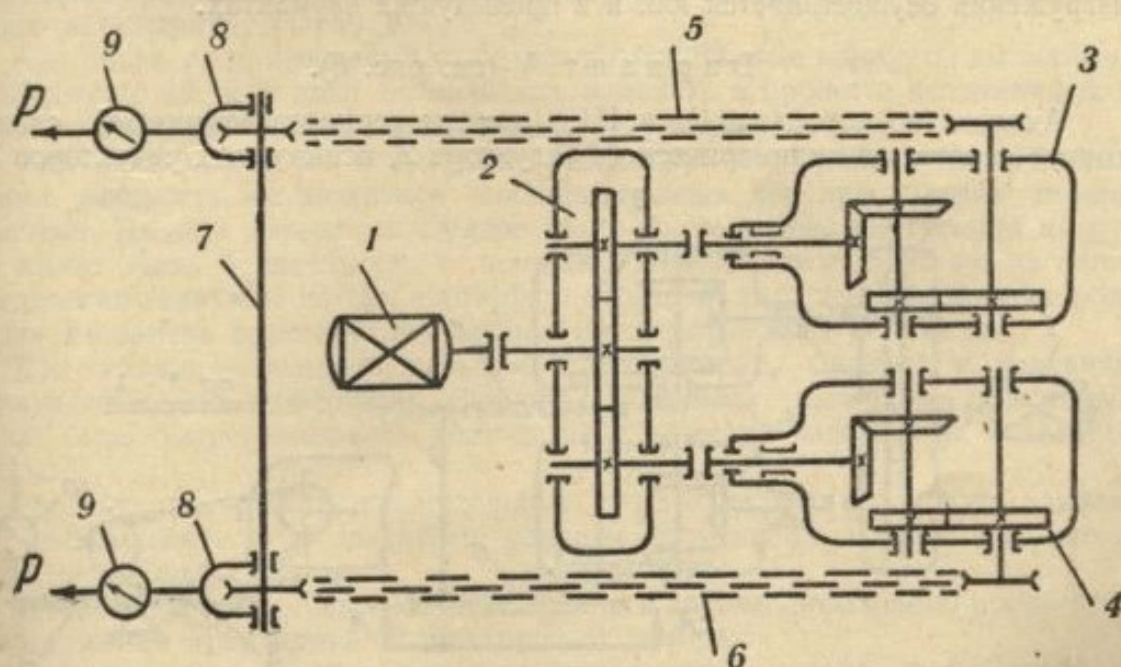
1 — Электродвигатель, 2 — цилиндрический редуктор, 3, 4 — испытуемые редукторы, 5, 6 — втулочно-роликовая цепь, 7 — промежуточный вал, 8 — подвижные опоры, 9 — динамометр.
